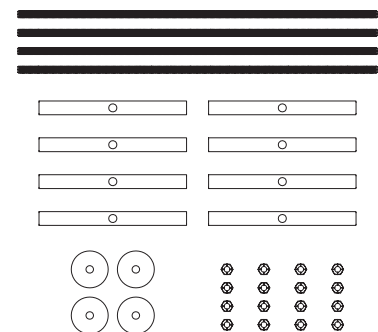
Conjunto de Montaje de Protector (2ATY1)
